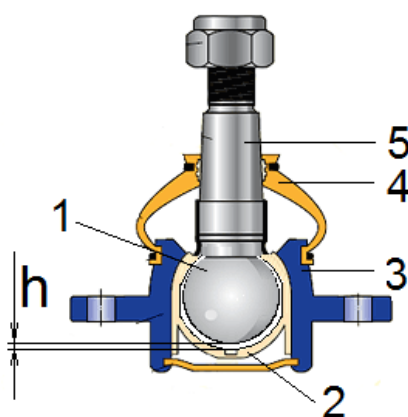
Общий вид шарового шарнира в разрезе:
